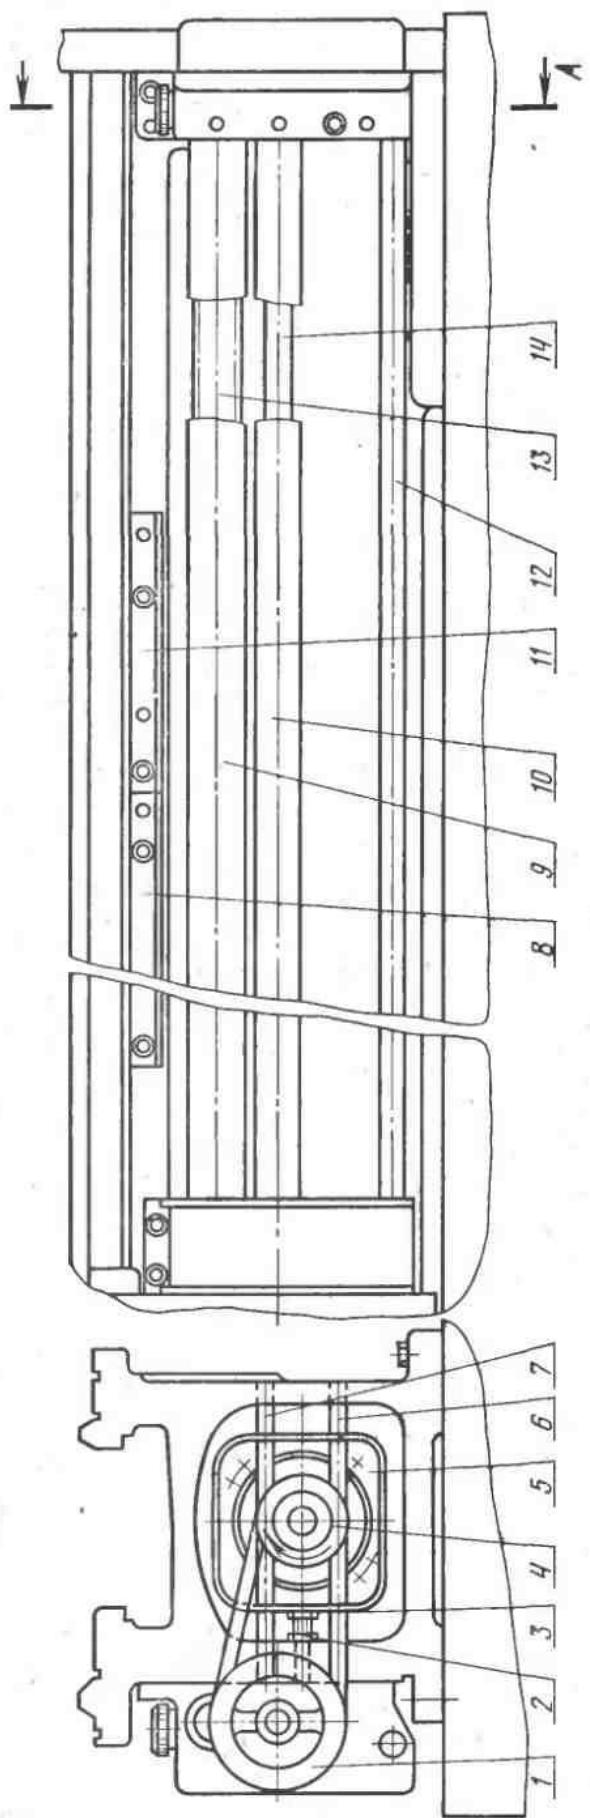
Станина, рейки, ходовой винт, ходовой вал и привод быстрых перемещений суппорта
